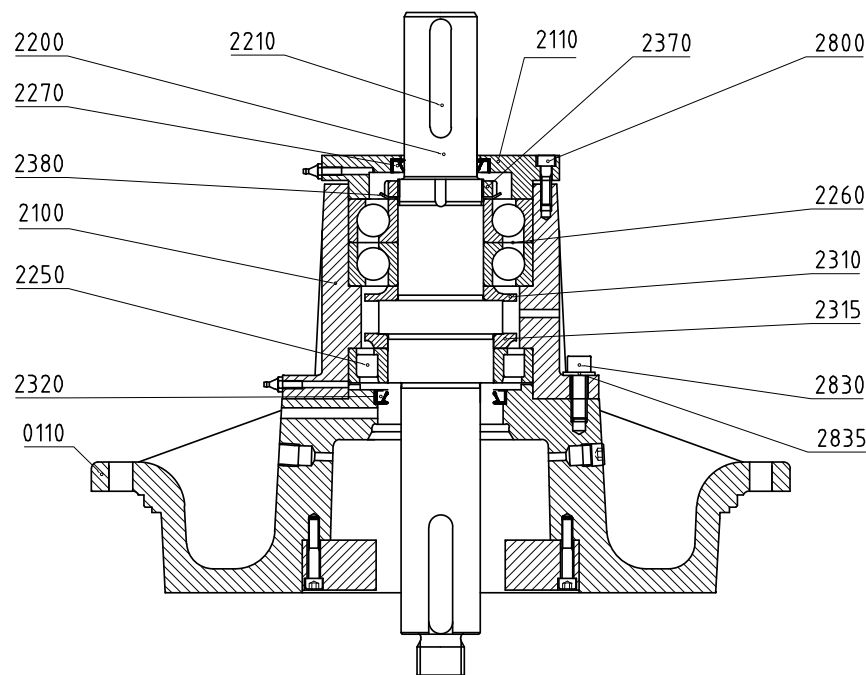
Разборка подшипников 200–400, 250–250, 250–315, 300–250, 300–315
